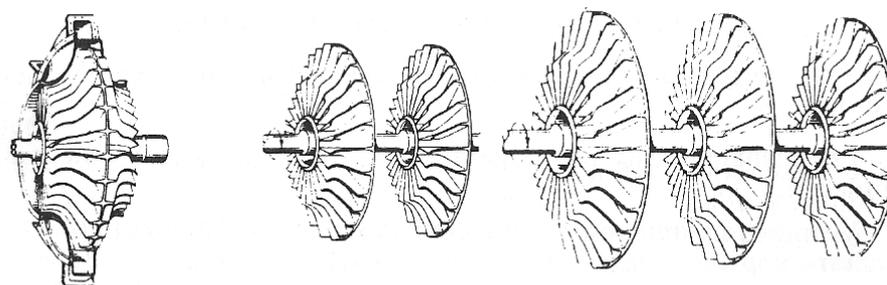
". - "Impellers" de distintos tipos de compresores centrífugos.
